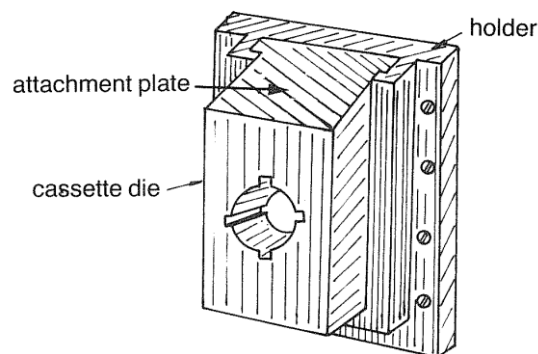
Metodo di interlocking per assicurare gli stampi
